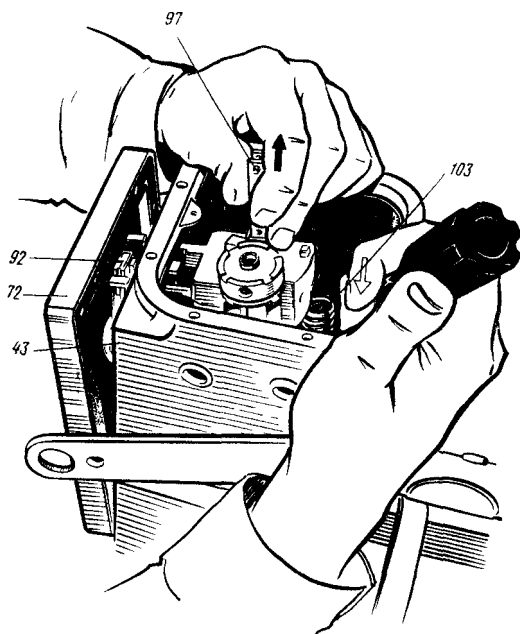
43— корпус; 72— панель; 92— планка ограничителя нагрузки; 97— рычаг регулирования неравномерности; 103— задающая пружина регулятора
